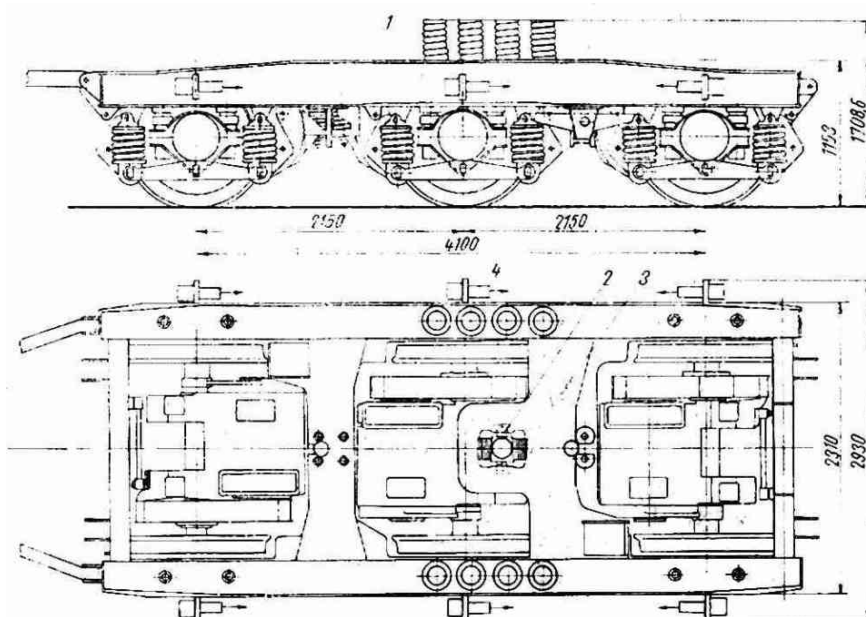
Boghiu de locomotivă diesel electrică LDE 060
